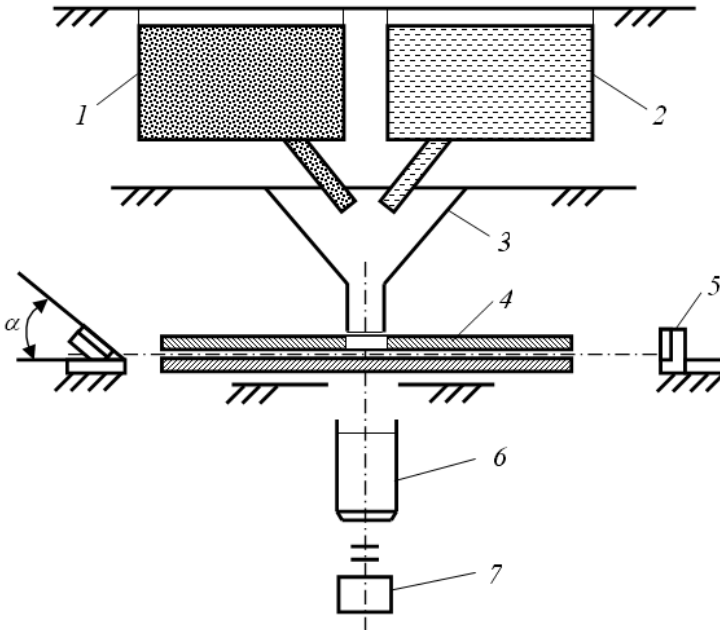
Схема відцентрового прискорювача: 1 – резервуар з абразивними частинками; 2 – резервуар з технічною водою; 3 – бункер для змішування суміші; 4 – ротор; 5 – зразок з покриттям; 6 – електродвигун; 7 – тахометр.
